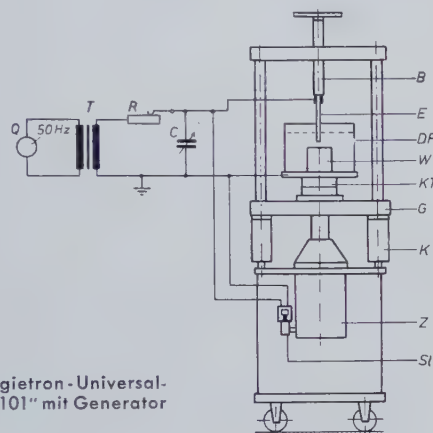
Prinzipbild der Agietron-Universalwerkzeugmaschine „UFE/2K/101“ mit Generator
